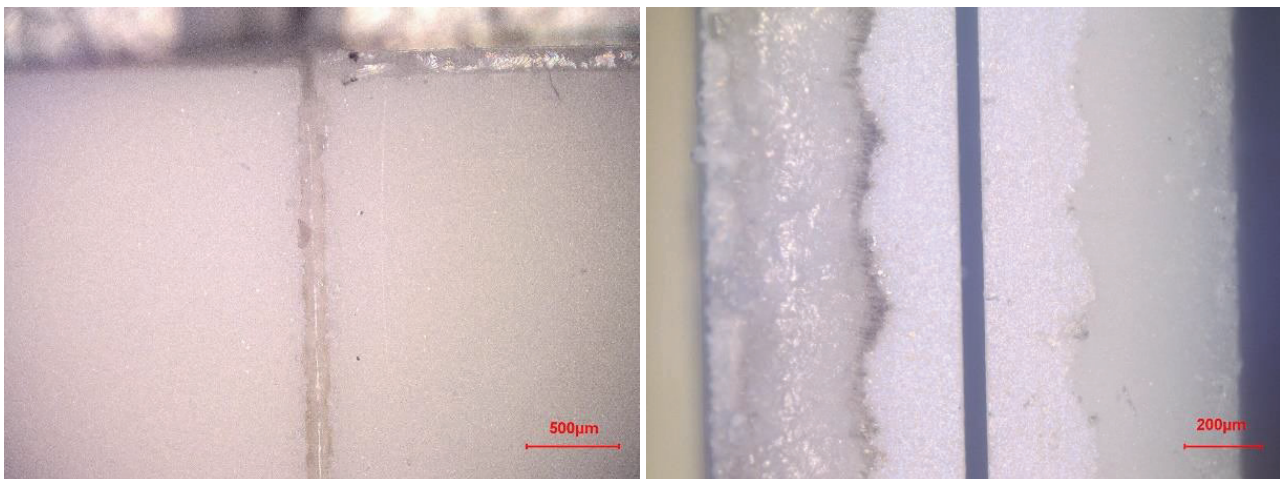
Erste Versuchsergebnisse zum Keramikschiweißen. Links: Draufsicht auf die Schweißnaht, rechts: Bruchbild der Schweißnaht entlang der Fügezone
